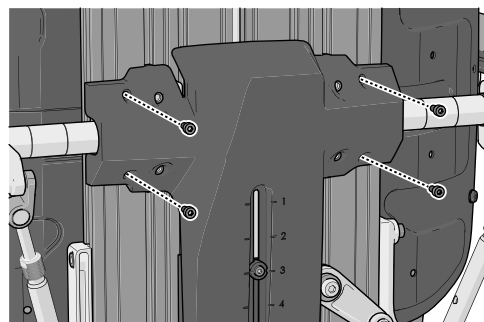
Die Anbringungsorte der vier Schrauben, die die Kunststoffabdeckung sichern.
